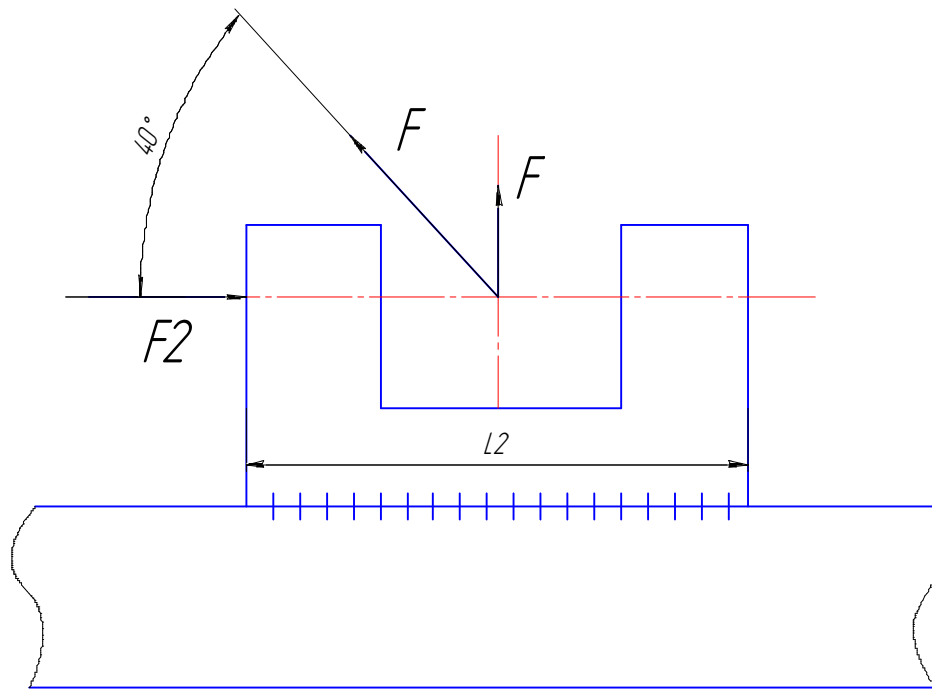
Розрахункова схема зварного шва кронштейна регулювальної планки
